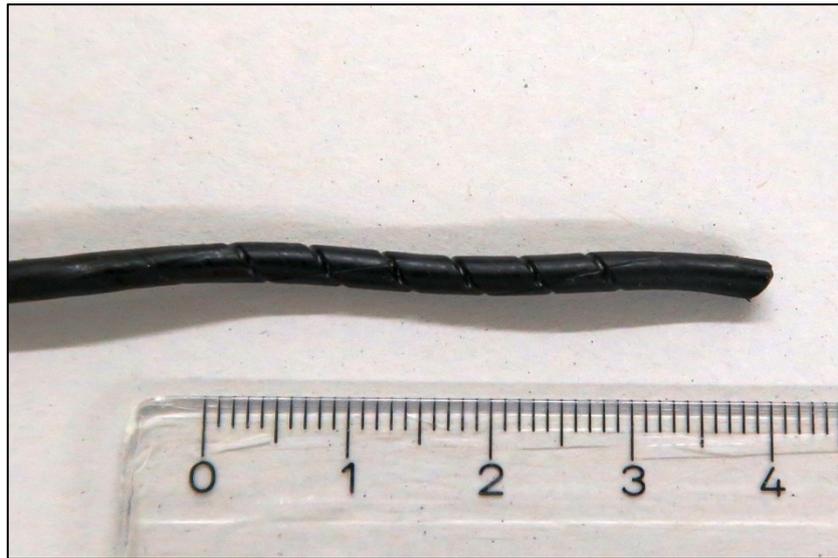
gerissener O-Ring mit Einkerbungen
